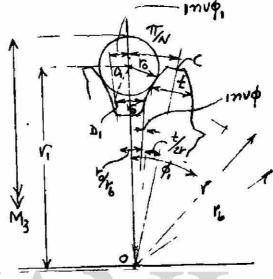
Espesor del dien rodillos para un No. par de dientes.
